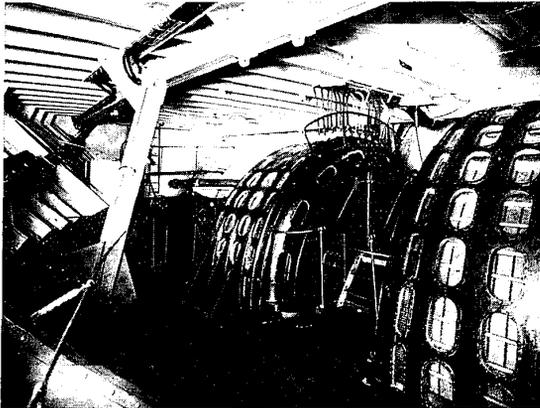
Compartment des moteurs. Vue latérale.
